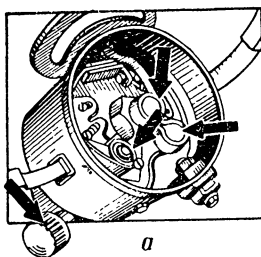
Точки смазки, смазываемые маслом для двигателя:
